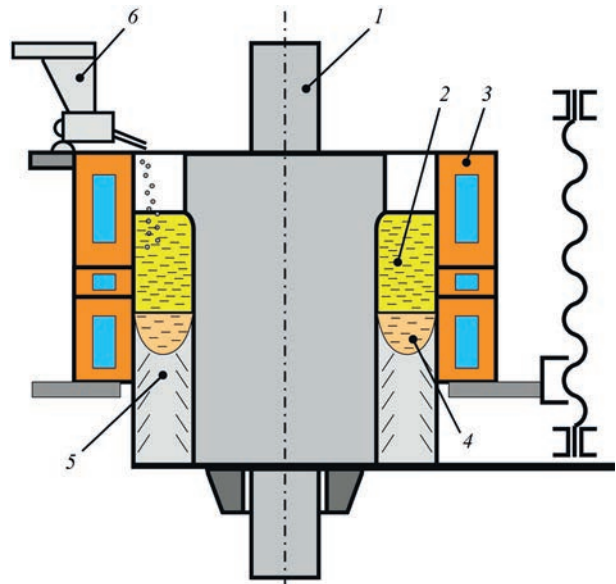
ЕШН прокатних валків у струмопровідному кристалізаторі з присаджувальним матеріалом у вигляді дробу: 1 – прокатний валок; 2 – шлакова ванна; 3 – струмопровідний кристалізатор; 4 – металева ванна; 5 – напавлений шар; 6 – дозатор із дробом
